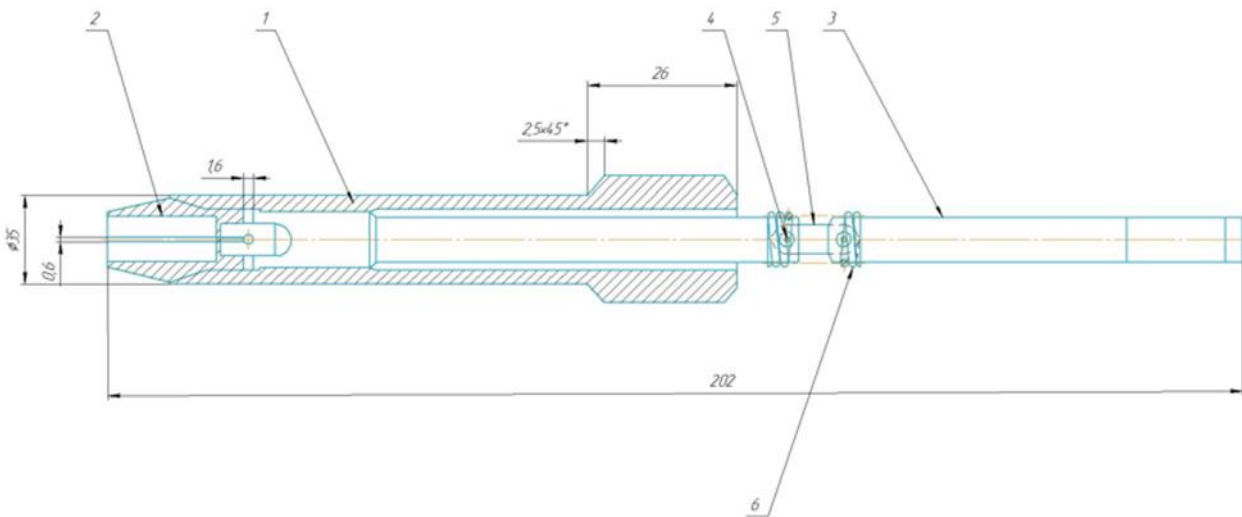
Цанговое приспособление для притирки клапанов ГБЦ ДВС:
